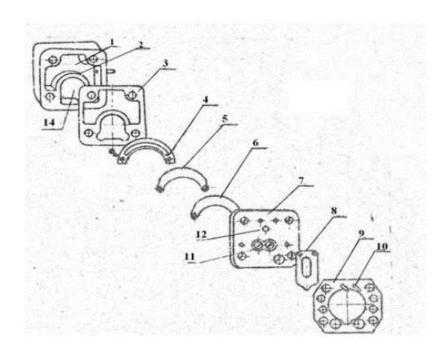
Крышка блока цилиндра и клапанная группа герметичного компрессора:
